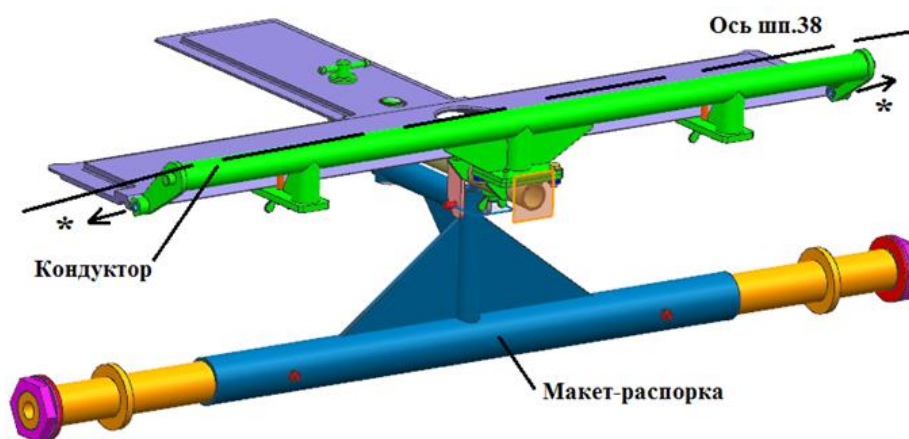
Кондуктор для пробития отверстий в обшивках
